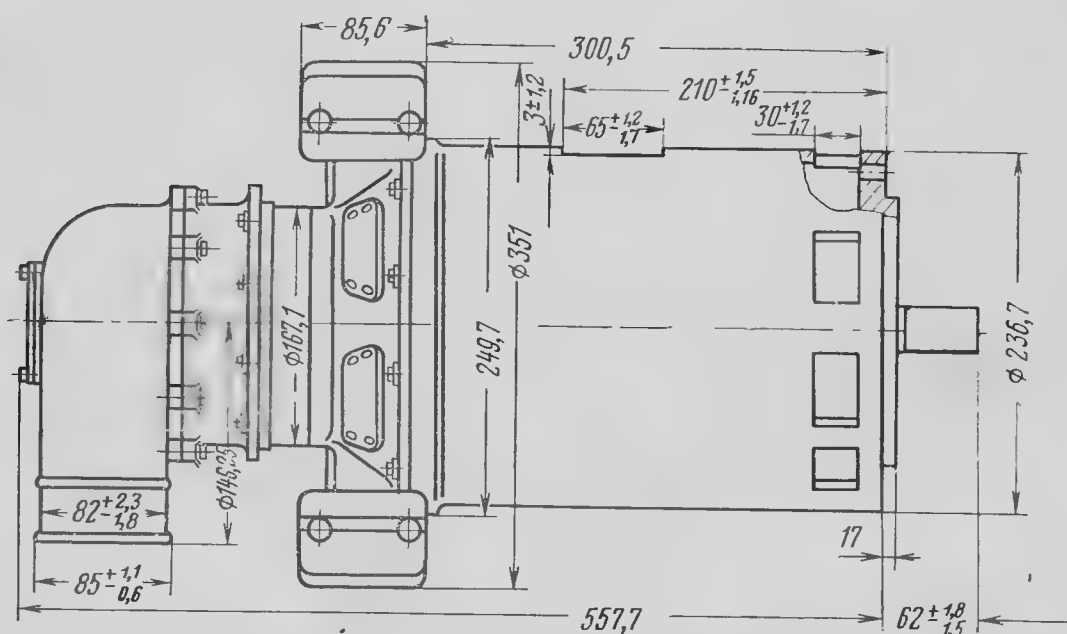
Габаритные и установочные размеры генератора СГС-90/360 2с
